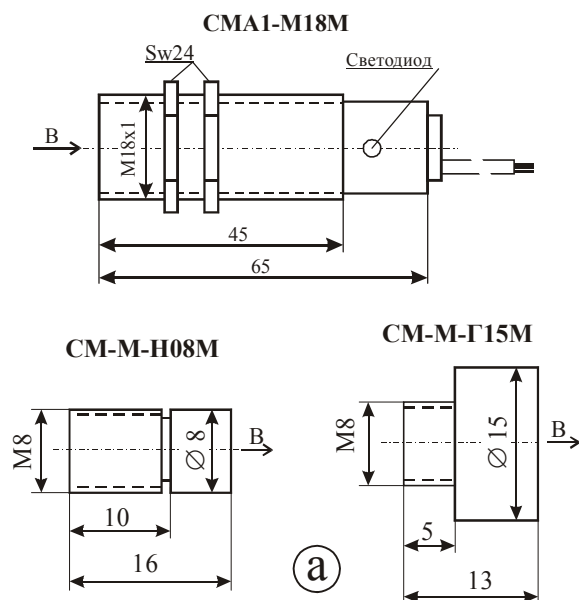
Внешний вид и габаритные размеры датчиков типа СМА1-М18М
